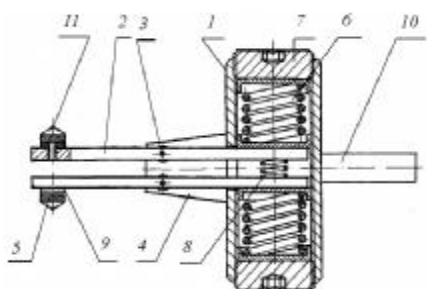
Пристрій для накатування канавок на внутрішніх циліндричних поверхнях: 1 – корпус; 2 – важіль; 3 – вісь; 4 – опора; 5 – ковпачок; 6 – пружина; 7 – гайка; 8 – пружина; 9 – опора; 10 – оправка; 11 – кулька
